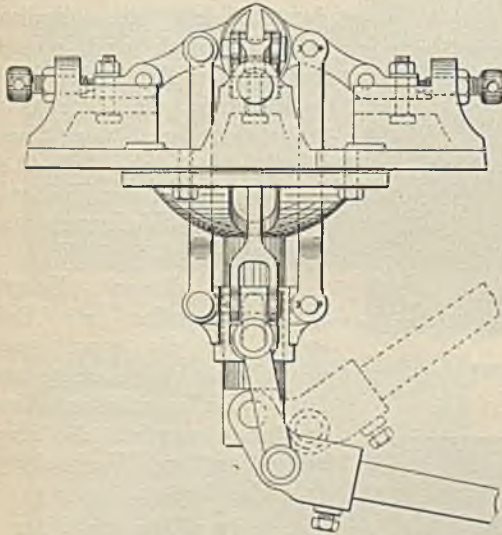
Eccles-Ballmaschine mit 4 Backen, geschlossen, in Seitenansicht
